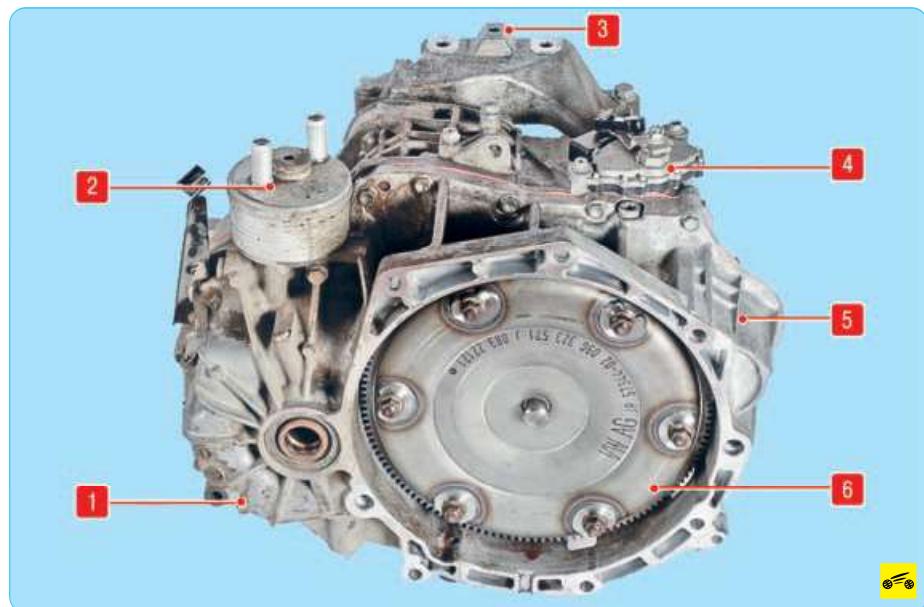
Автоматическая коробка передач: 1 – картер редуктора главной передачи; 2 – теплообменник рабочей жидкости; 3 – кронштейн левой опоры подвески силового агрегата; 4 – датчик положения селектора; 5 – кожух гидротрансформатора; 6 – гидротрансформатор
